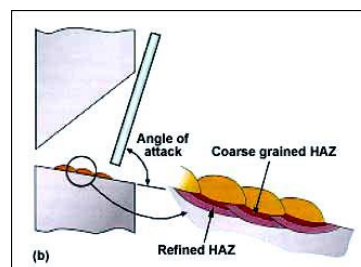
Soudage en position à plat – haut verticale ou horizontale – faible Degré de raffinement de la ZAT.
